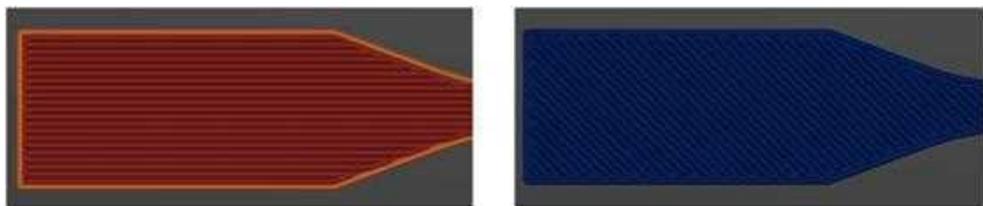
Infil rettilineo (sx) e diagonale (dx).
